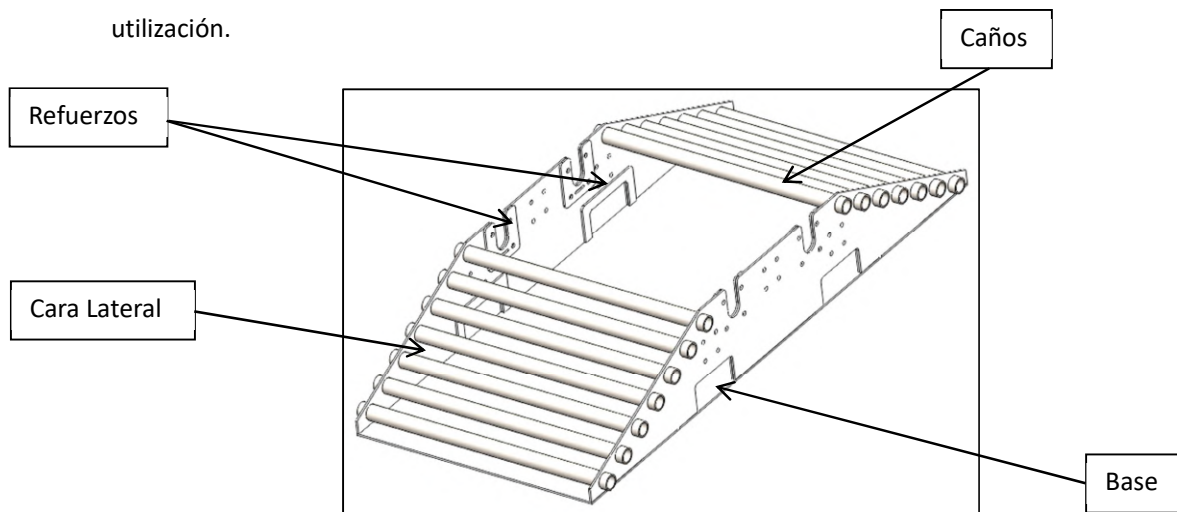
Vista isométrica de conjunto soldado del cajón
